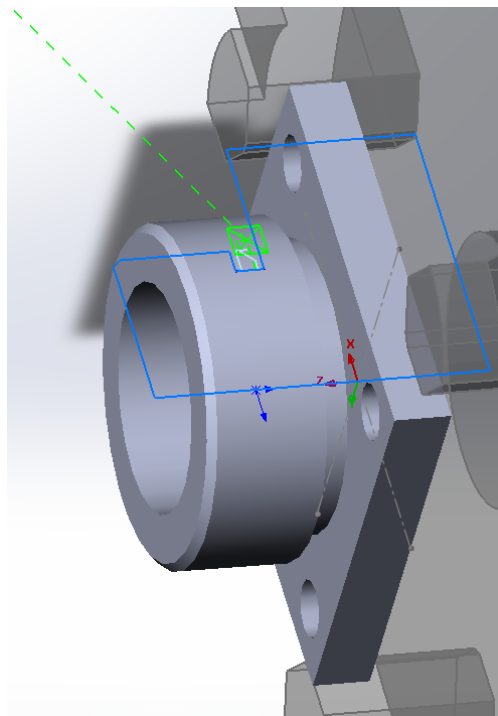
Траєкторія обробки поверхні 8 на токарному верстаті з ЧПК
